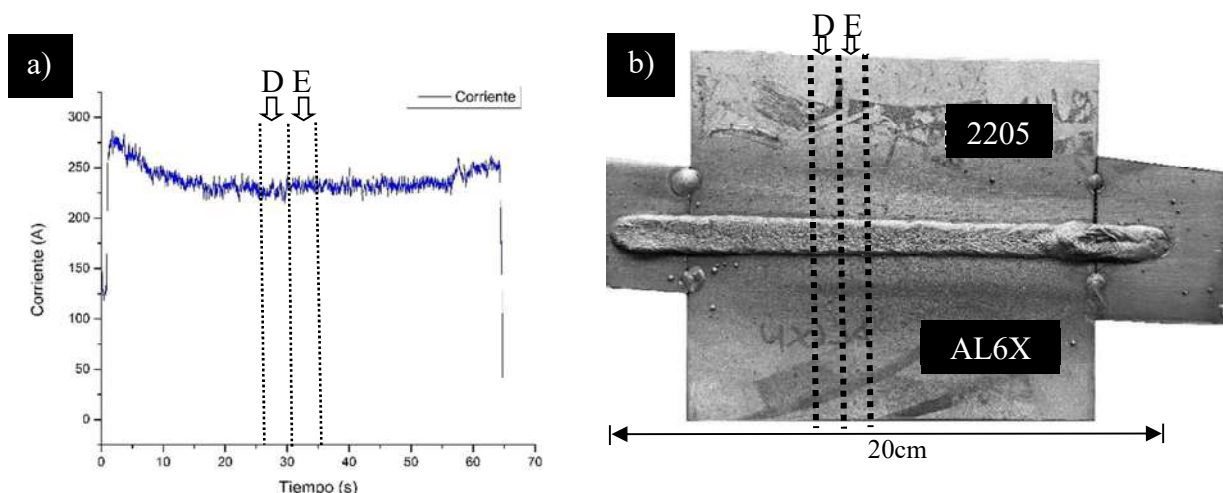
Junta soldada OTC DP400 GMAW pulsado. a) comportamiento de la corriente en modo sinérgico durante el proceso de soldadura, y b) placa soldada (regiones caracterizadas).
